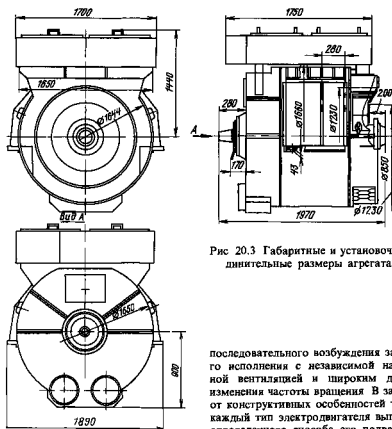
Габаритные и установочно-присоединительные размеры агрегата А714А
